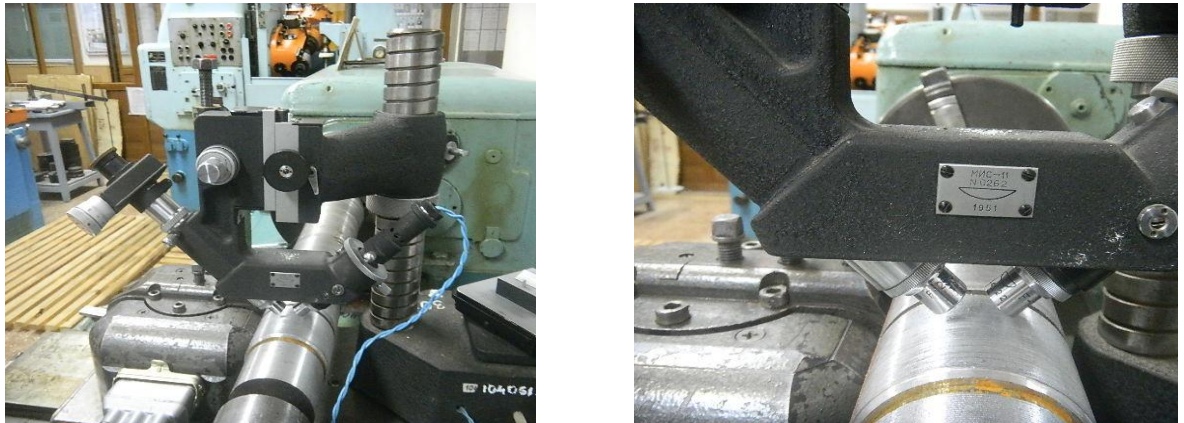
Мікроскоп МІС-11 для вимірювання шорсткості обробленої поверхні
